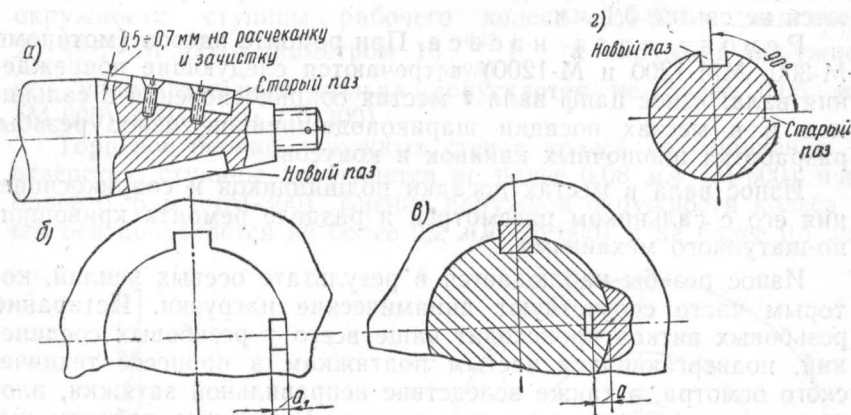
Схема изготовления шпоночного паза на новом месте:
